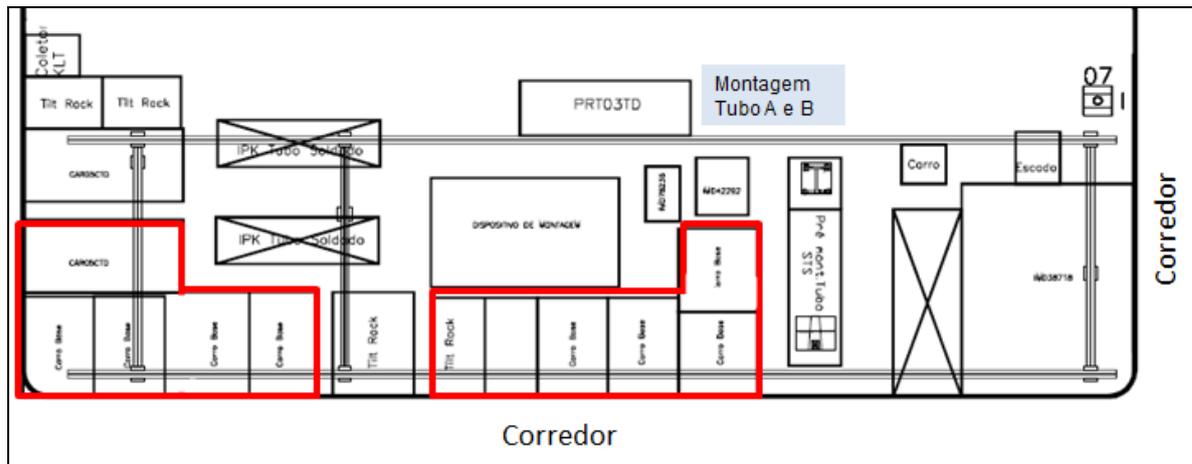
Localização da célula de soldagem e transporte do tubo A e B
